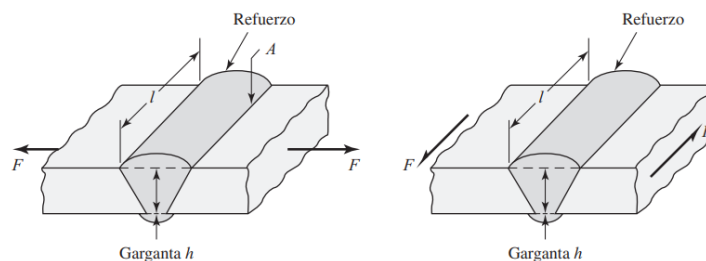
Soldadura sometida a tensión y a cortante, de izquierda a derecha [7].
